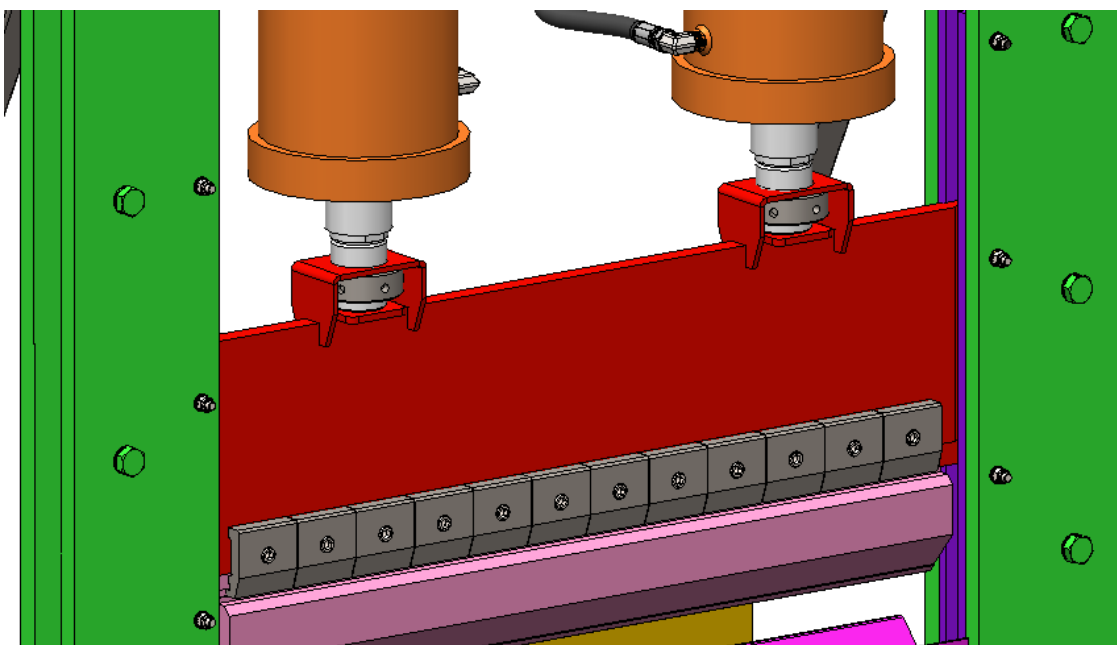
Detalle conexión cilindros – delantal y punzón-delantal.
